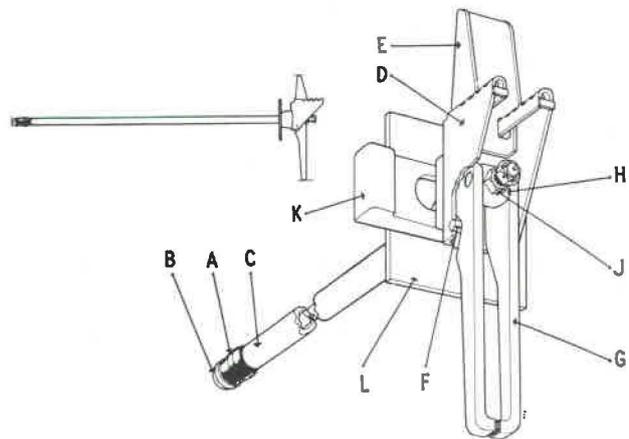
Boulon récupérable Dowty utilisé pour le calage des bossements.
